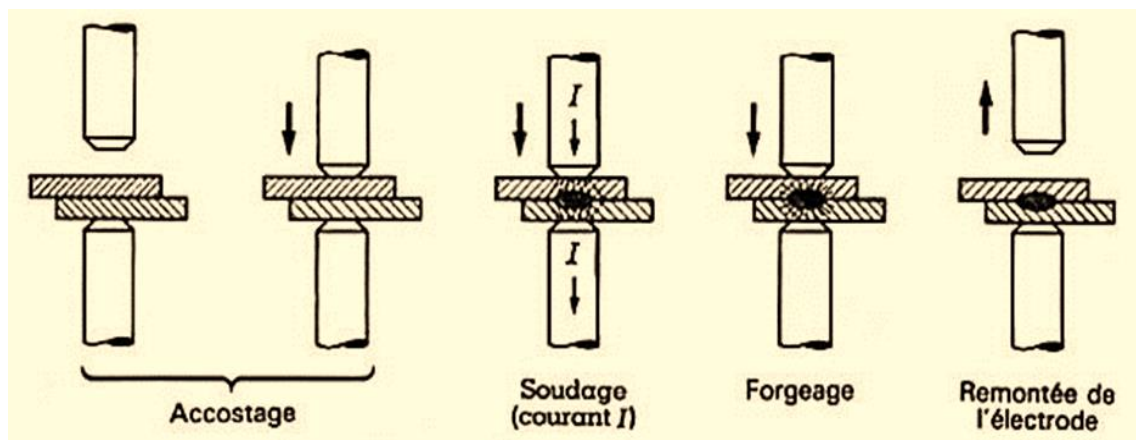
Mécanisme du soudage par point. [5]
